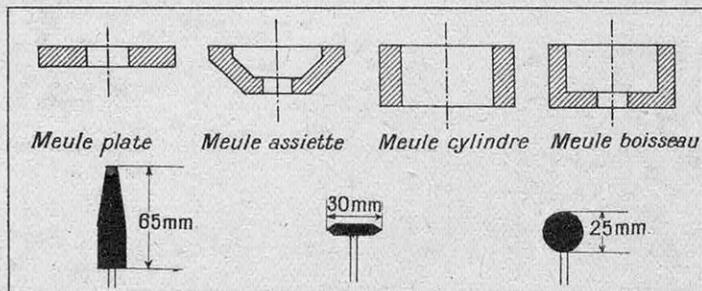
QUELQUES FORMES COURANTES DE MEULES
